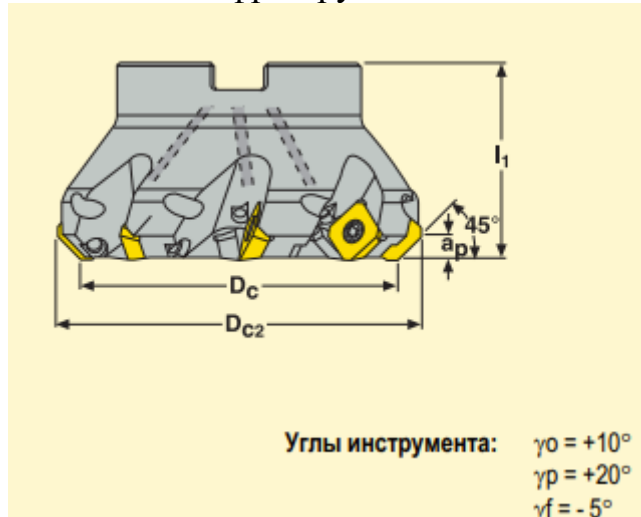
Фреза R220.53 -0050-12-5A [3, с.37]
